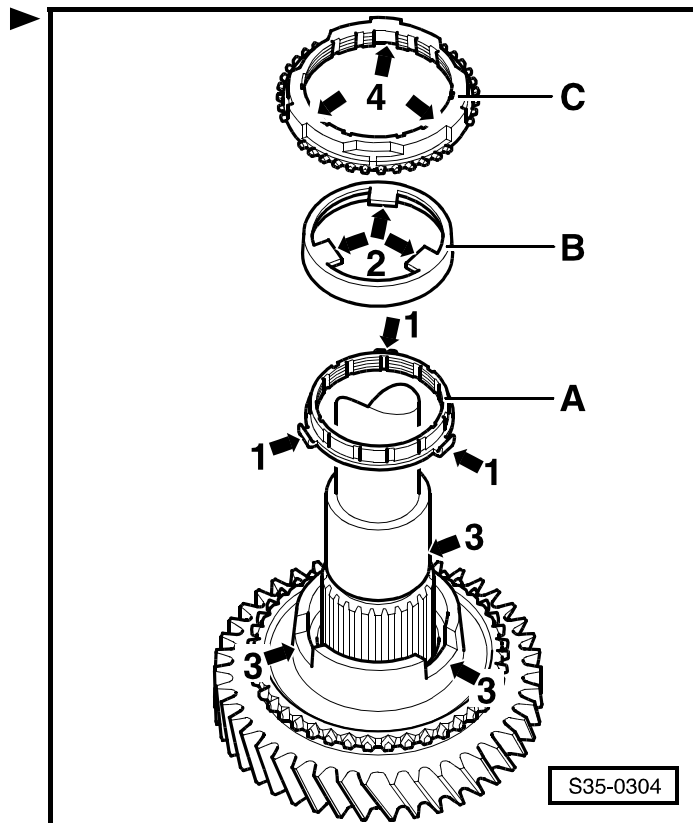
Разборка и сборка скользящей муфты и каретки синхронизатора 1-ой, 2-ой, 3-ей и 4-ой передач
